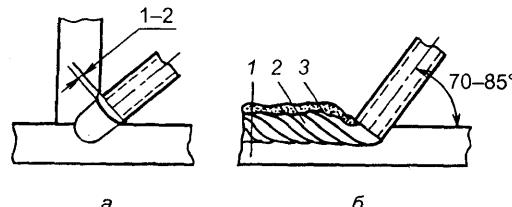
Сварка с опирианием электрода угловых (а) и стыковых (б) соединений:
